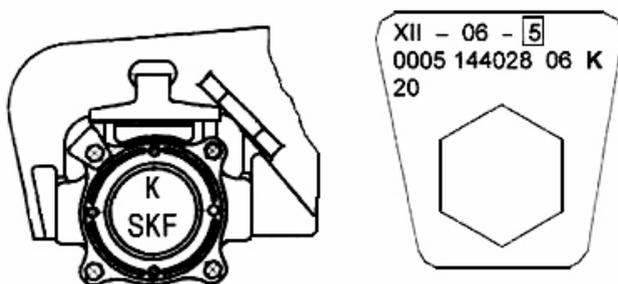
Маркировка буксового узла с подшипником кассетного типа:
